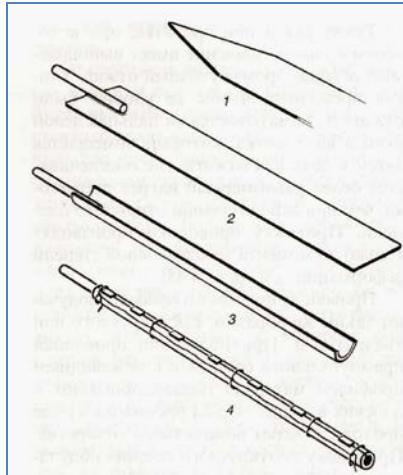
1 – Этапы изготовления трубчатой заготовки
